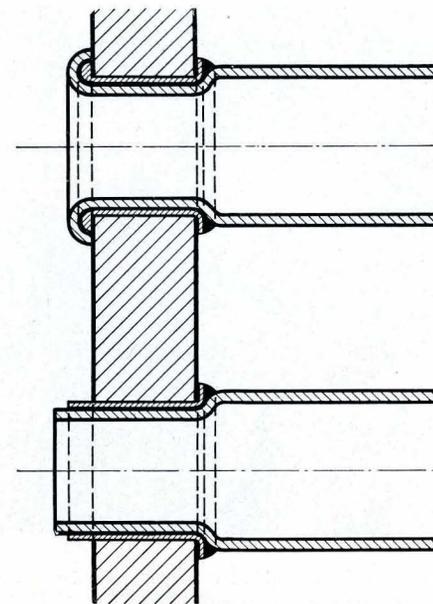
Befestigung der Rohre in der Feuerbüchsenwand mittels aufgelöteter Kupferlinge
